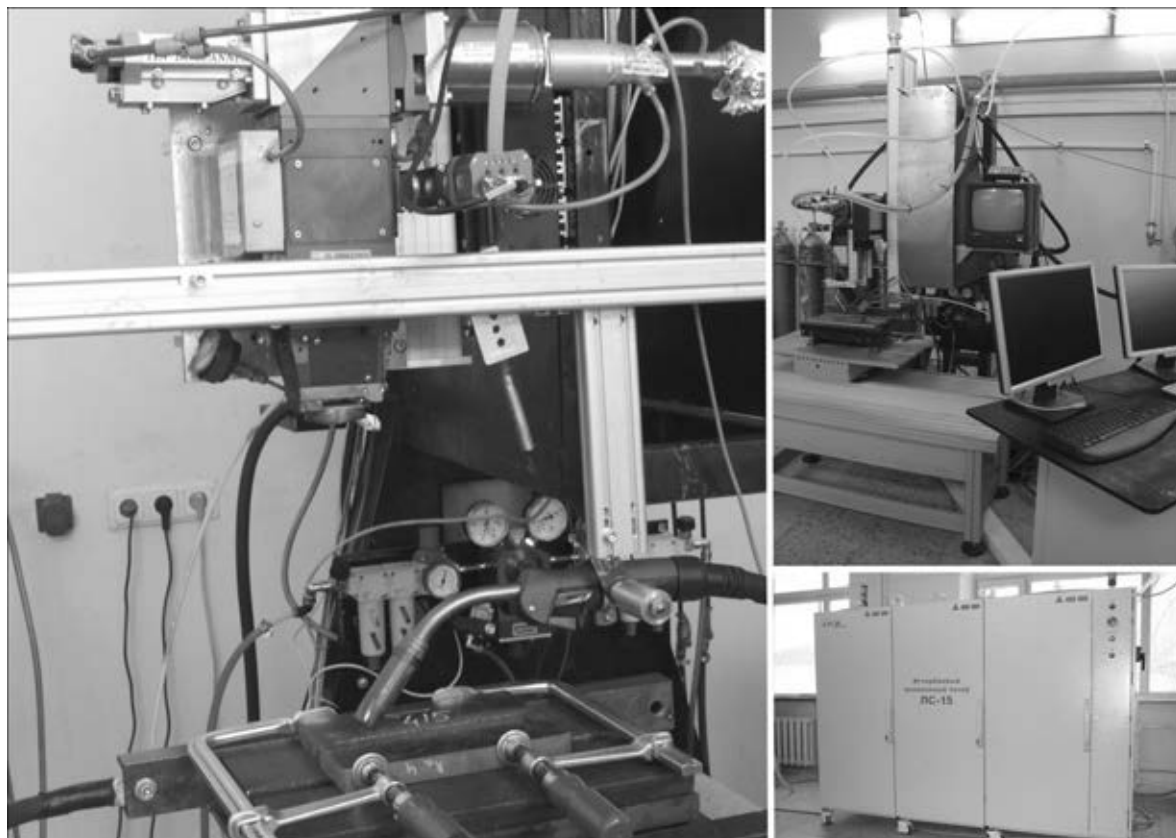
Фрагменты компоновки оборудования для лазерной сварки образцов стали толщиной 16, 20 мм (фокусное расстояние 400 мм, диаметр фокусного пятна 0,4 мм)
